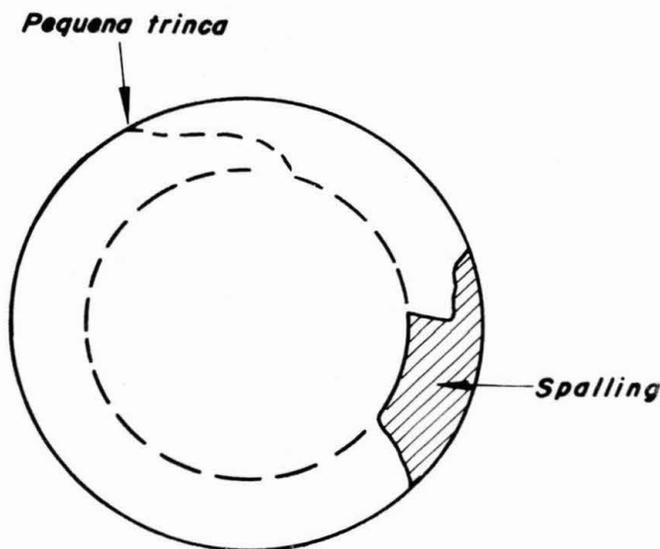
Perfil do desprendimento levantado por ultra-som
